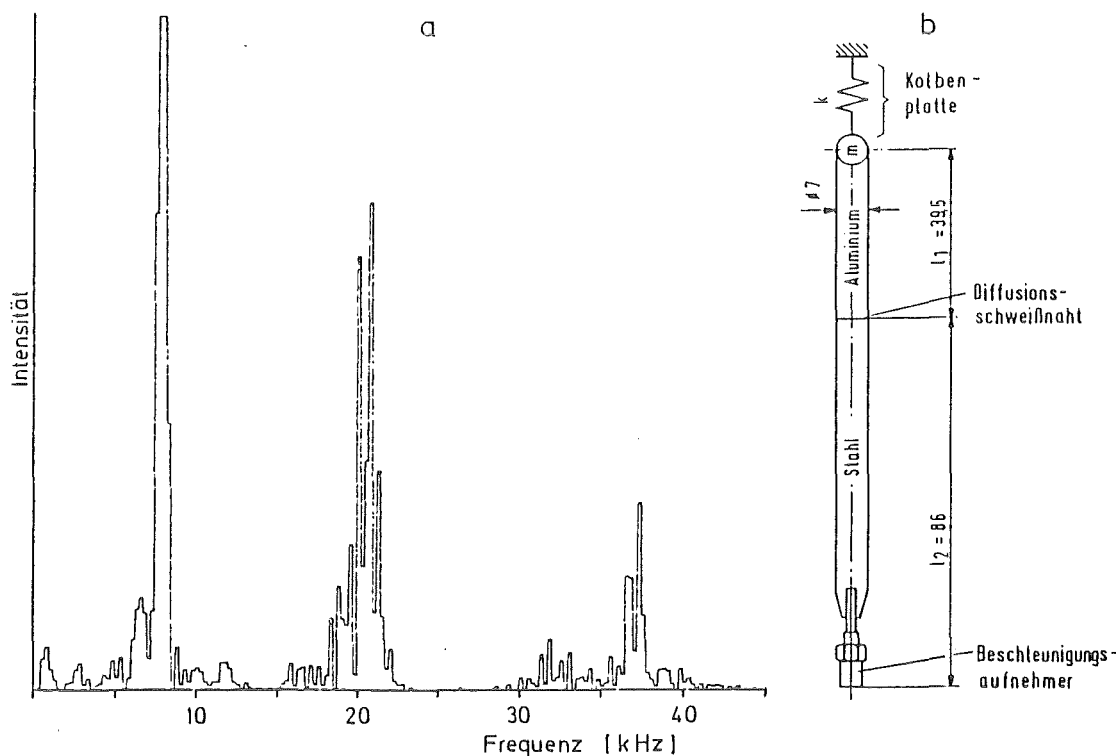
Frequenzspektrum der Kolbenstange ohne Probe (links), gemessen mit einem Beschleunigungsaufnehmer an der Probeneinspannung (rechts)
